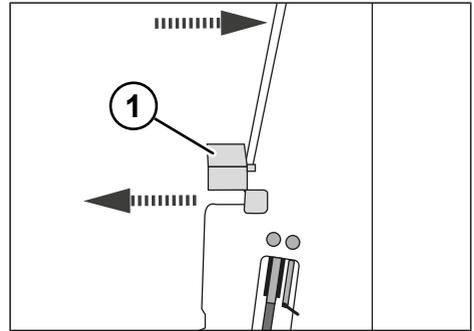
Fermo del bloccaggio nella posizione più elevata possibile
